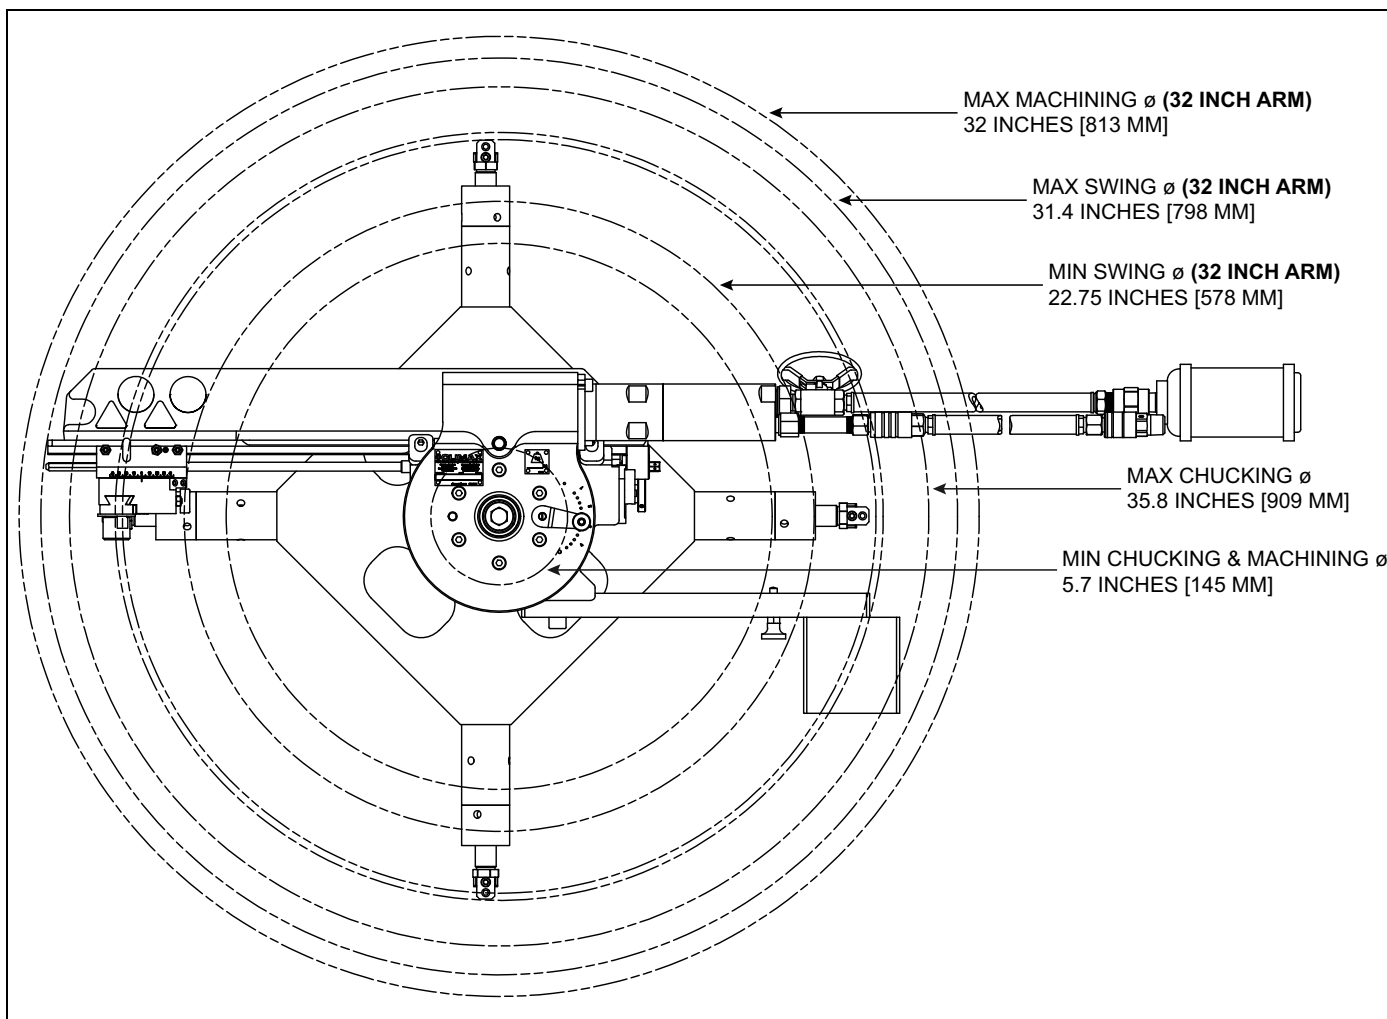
DIMENSIONS DU BRAS D'USINAGE 32" (813 MM)
